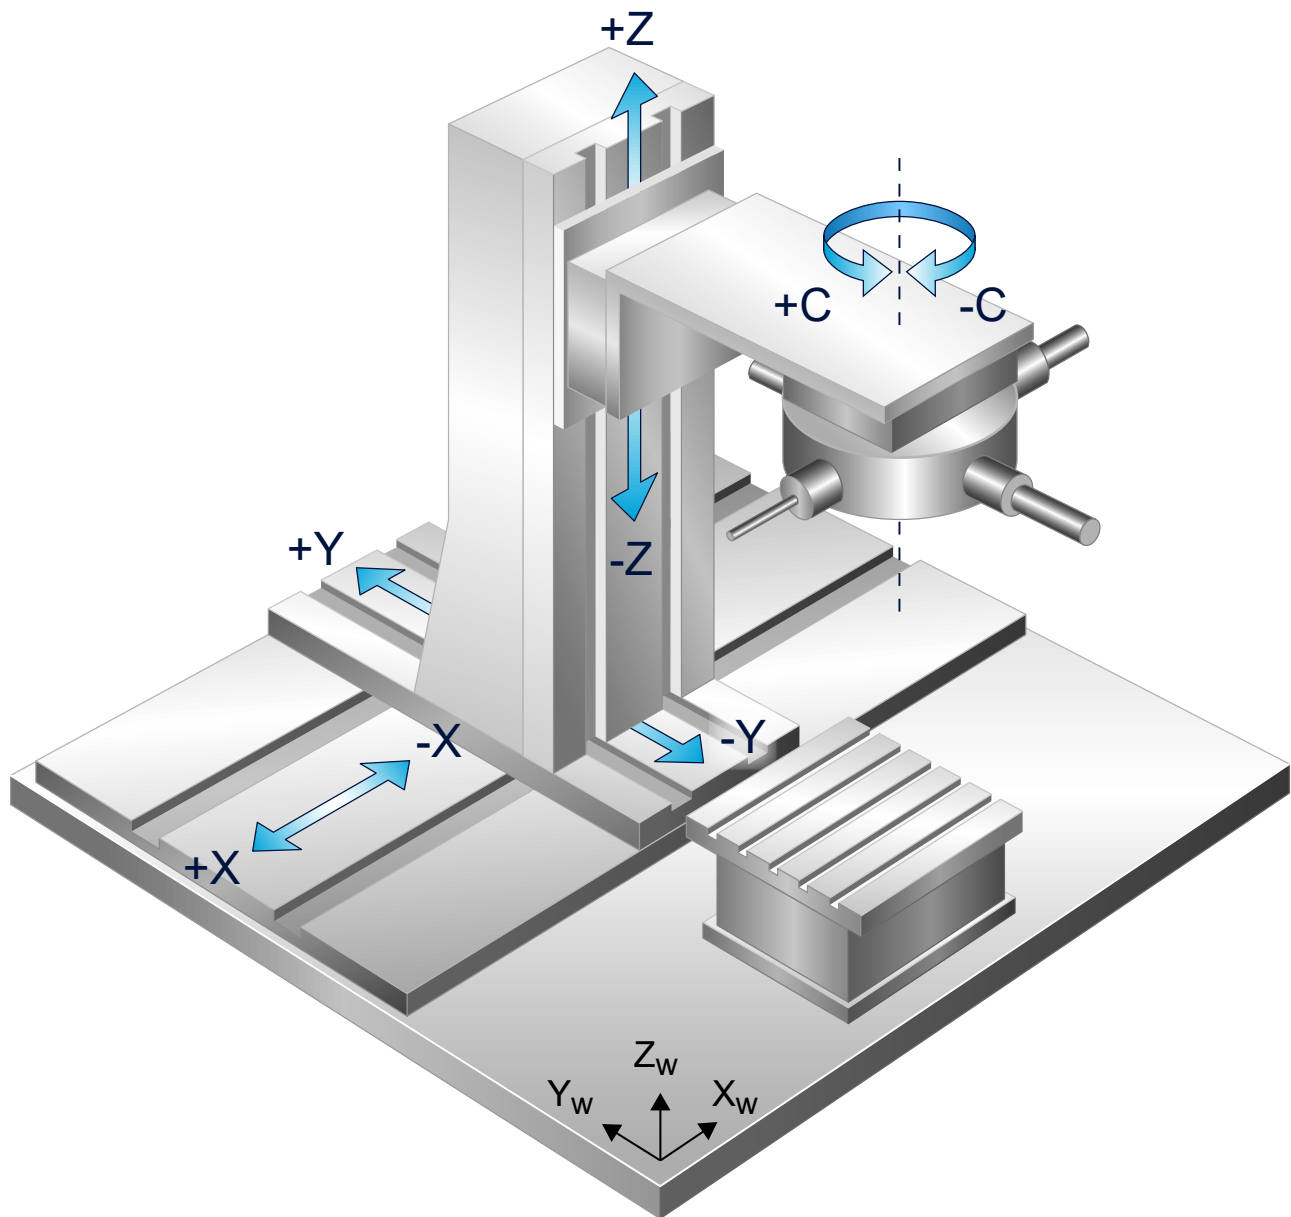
4-achsige Kinematik mit Kreuzkopf für 4 Werkzeuge
